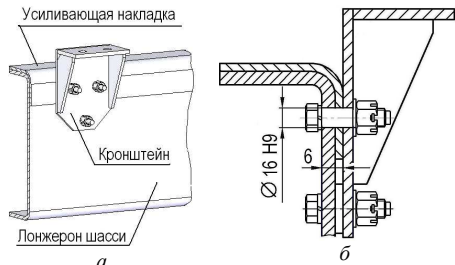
Узел крепления накладки к лонжерону шасси:
